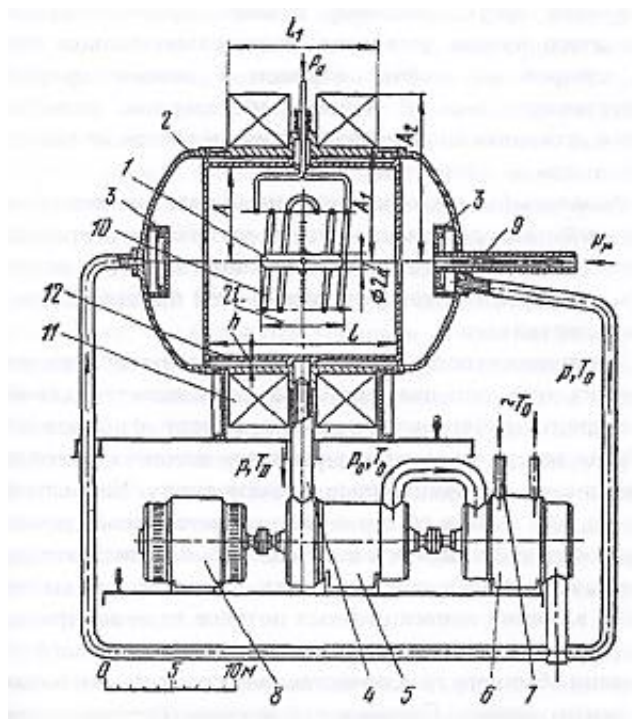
Чертеж конструкции термоядерного реактора, работающего в режиме замкнутого цикла: 1 – шнуровой разряд; 2 – цилиндрический контейнер реактора; 3 – наклонные сопла; 4 – труба, соединяющая контейнер реактора с газовой турбиной; 5 – газовая турбина; 6 – изотермический компрессор; 7 – охлаждающая вода; 8 – генератор; 9 – коаксиальный волновод; 10 – катушка переменного магнитного поля; 11 – соленоид; 12 – медный кожух резонатора.  $L$  – длина резонатора,  $L_1$  – длина соленоида,  $P_a$  – мощность магнитоакустических колебаний,  $P_c$  – высокочастотная мощность,  $A$  – радиус резонатора,  $A_1$  – внутренний радиус обмотки,  $A_2$  – наружный радиус обмотки,  $2l$  – длина шнурового разряда,  $2a$  – диаметр шнурового разряда,  $h$  – расстояние между стенкой контейнера и резонатором
